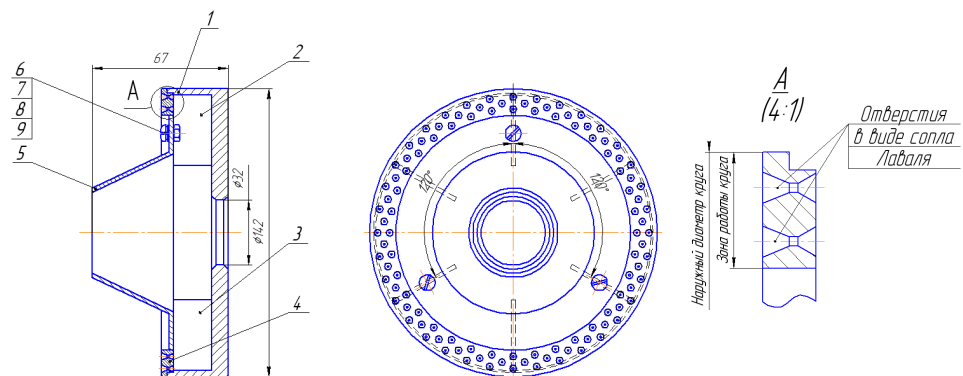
Алмазный круг с отверстиями на рабочей поверхности, выполненными в виде сопла Лавала (СБОРКА: 1 – корпус; 2 – лопасть с гайкой; 3 – лопасть без гайки; 4 – кольцо; 5 – крышка; 6 – винт М4 6 ГОСТ 11644–75; 7 – стопорная шайба 4; 8 – шайба ГОСТ 9649–78; 9 – гайка М4 ГОСТ 5927–70)
